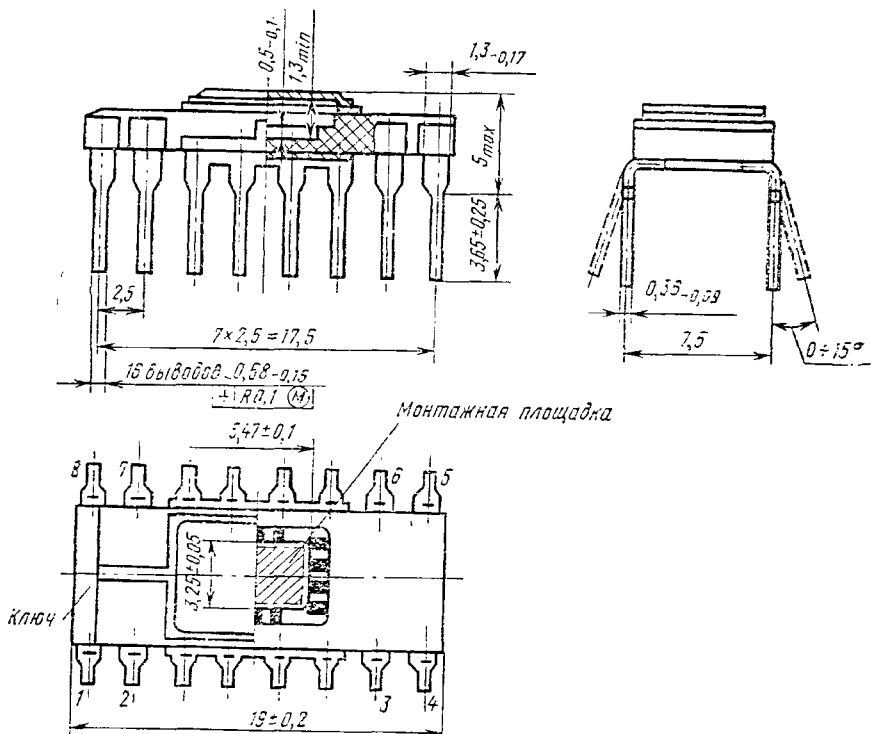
Конструкция металлокерамического корпуса 2103 (2018-1)
